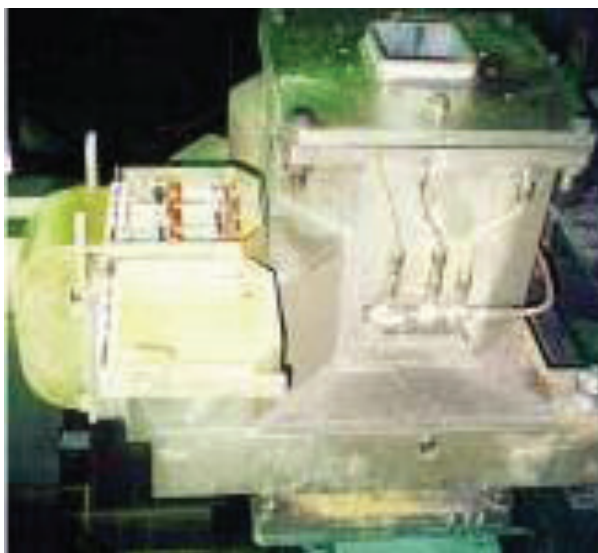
Внешний вид электромагнитного кристаллизатора конструкции ВНИИМЕТМАШ - ЗАО "ЭМТ"
